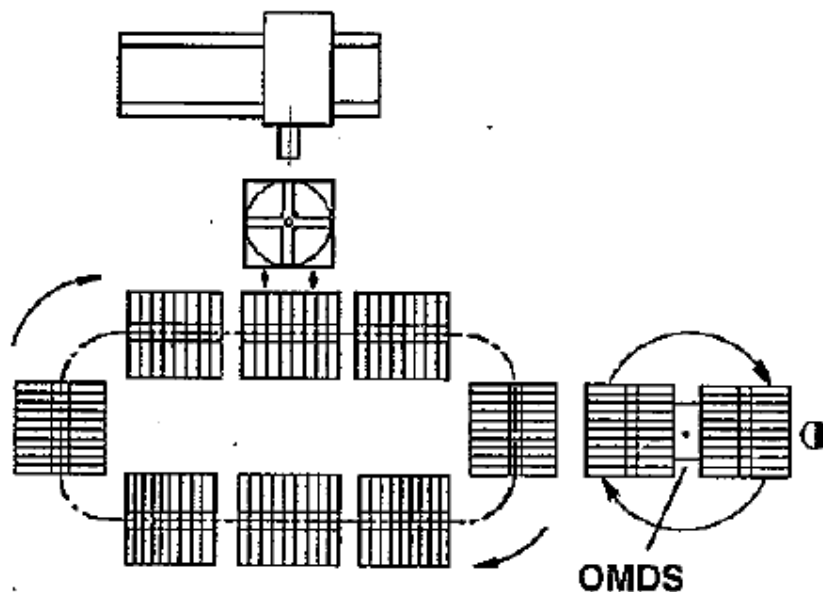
Manipulator za izmjenu paleta između više obradnih strojeva [21]
